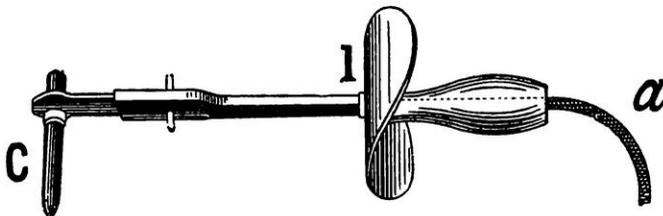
APPAREIL BERNADOT POUR LA SOUDURE PAR L'ARC ÉLECTRIQUE
